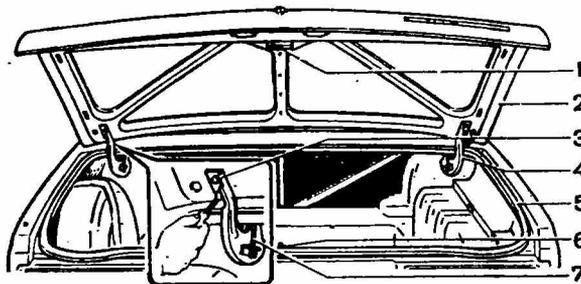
Снятие крышки багажника: 1 - замок крышки; 2 - крышка багажника; 3 - гайка крепления петли; 4 - петля; 5 - уплотнитель крышки багажника; 6 - фиксатор замка; 7 - торсион
